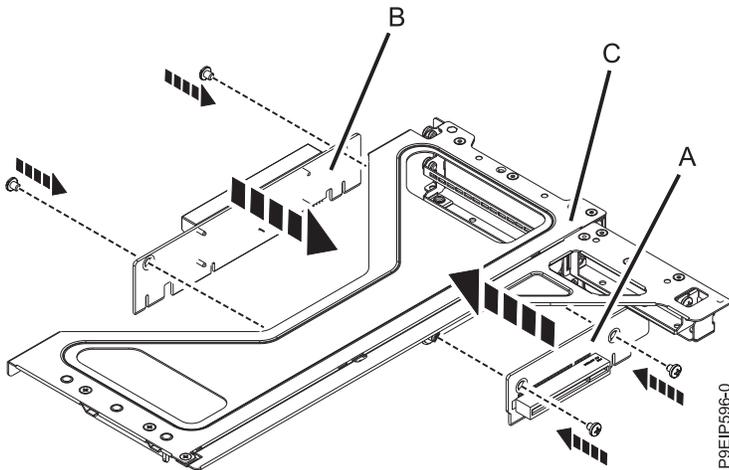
Cómo volver a colocar las tarjetas de expansión PCIe en la caja del adaptador PCIe
